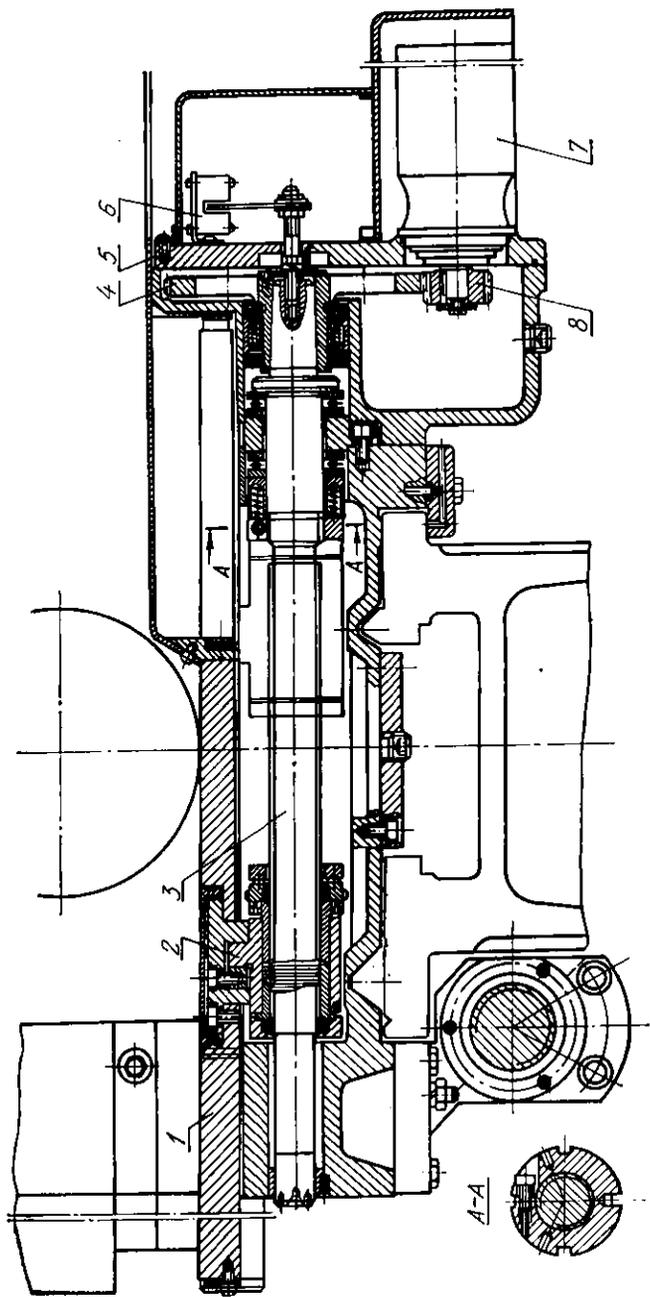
Привод поперечной подачи токарного станка модели 16К20Ф3С4
